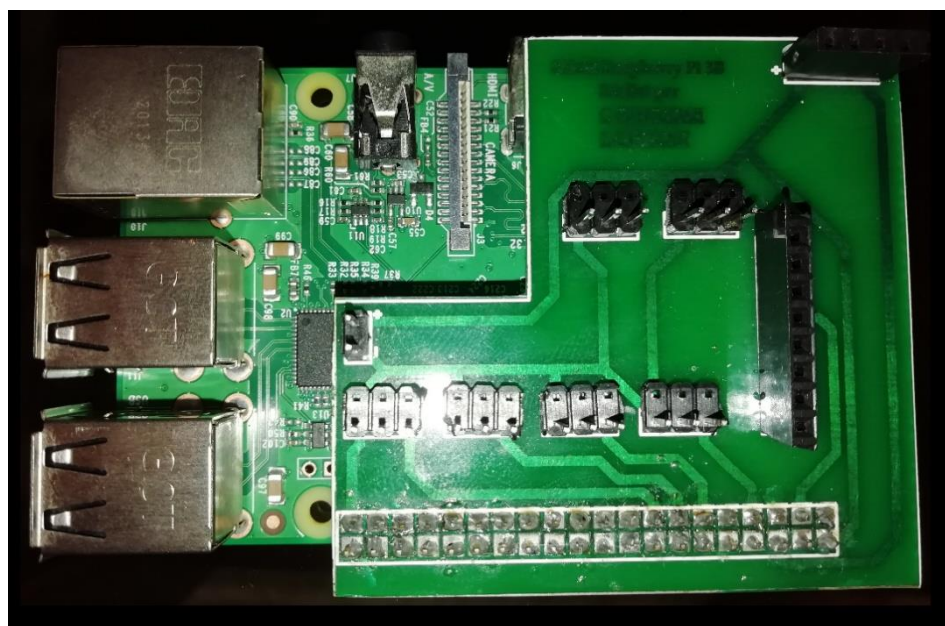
Montage de PCB avec Raspberry Pi 3B
